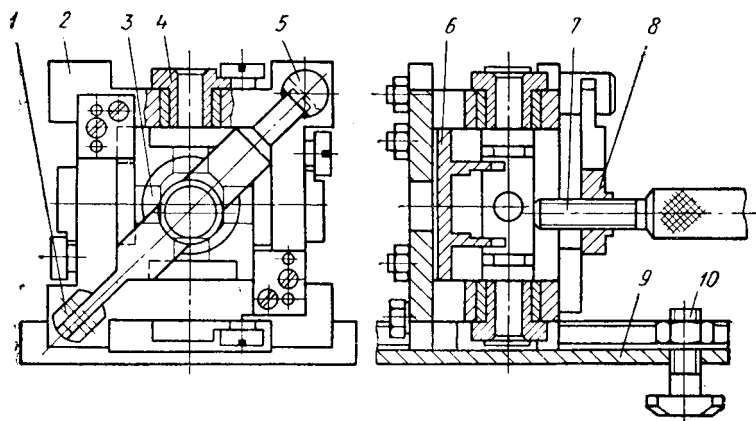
Кантующееся приспособление для зацентровки крестовин
